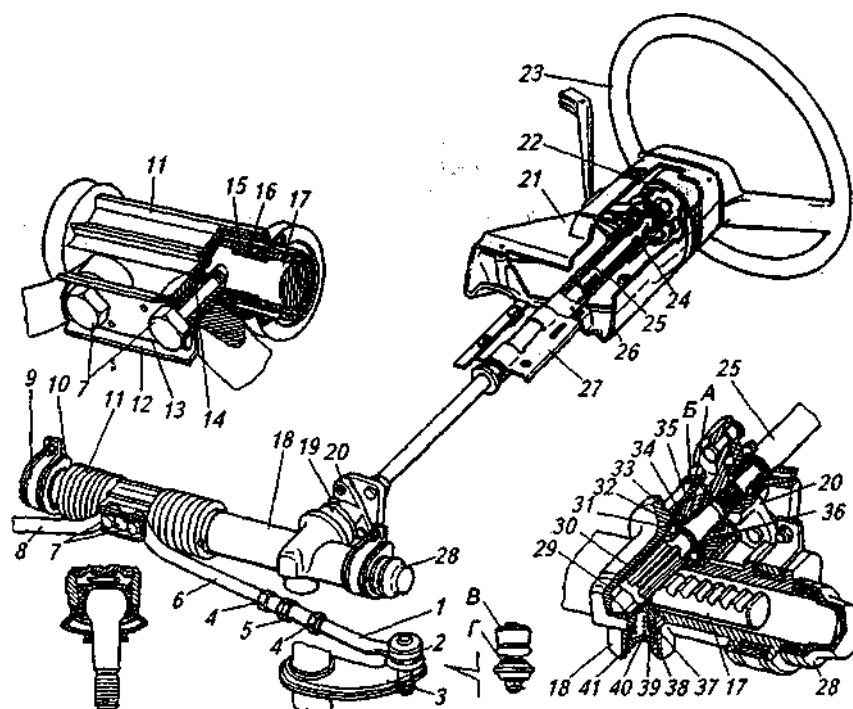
Реечный рулевой механизм: 1 — наконечник тяги; 2 — шаровой шарнир; 3 — поворотный рычаг; 4 — гайка; 5 — трубчатая тяга; 6, 8 — тяги; 7 — болты; 9 — скоба; 10 — резиновая опора; 11 — защитный чехол; 12 — соединительная пластина; 13 — стопорная пластина; 14 — резинометаллический шарнир; 15 — уплотнительное кольцо; 16 — втулка; 17 — рейка; 18 — картер рулевого механизма; 19 — стяжной болт; 20 — эластичная муфта; 21 — кожух; 22 — демпфирующий элемент; 23 — рулевое колесо; 24 — подшипник; 25 — вал; 26 — кожух; 27 — кронштейн; 28 — защитный колпачок; 29, 31 — подшипники; 30 — шестерня; 32 — стопорное кольцо; 33 — защитная шайба; 34 — уплотнительное кольцо; 35 — гайка; 36 — чехол; 37 — резиновое кольцо; 38 — стопорное кольцо; 39 — упор; 40 — пружина; 41 — гайка.
